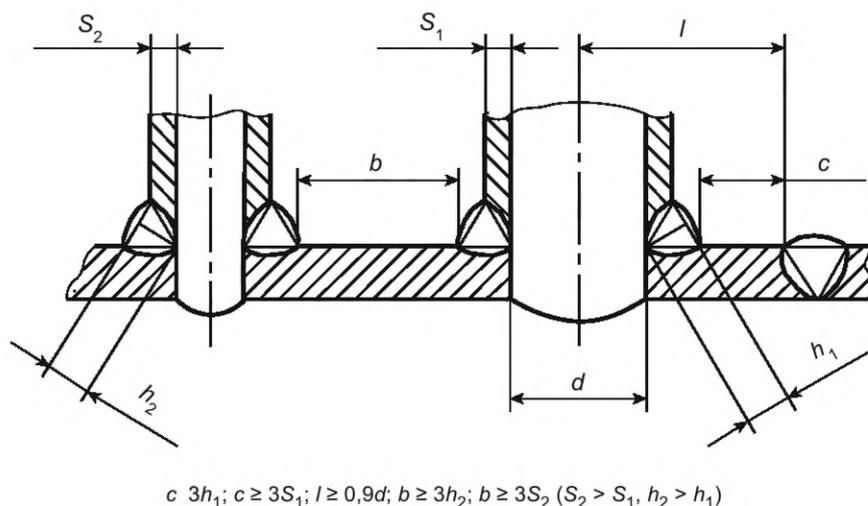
Расположение сварных соединений приварки патрубков
